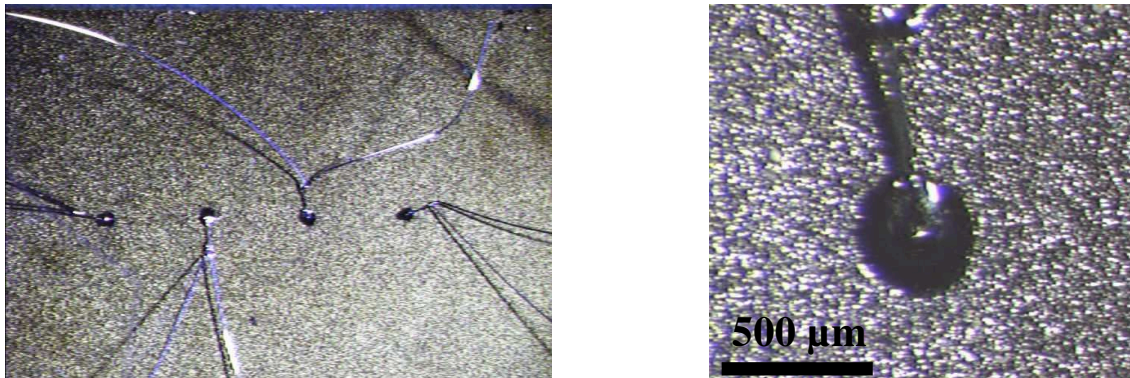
Wolfram-Silizium Kontakte Wolframdraht (Drahtdurchmesser 50 µm). Konfiguration zur Kontaktwiderstandsmessung (links) und vergrößerte Aufnahme eines Laserschweißpunktes mit Wolfram-Draht und angeschweißtem Thermoelement.
